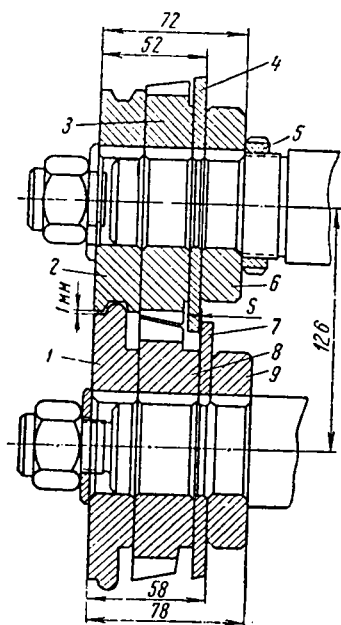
Комплект роликов к зигмашине ЗМ-4 для изготовления гофра и валика жесткости
